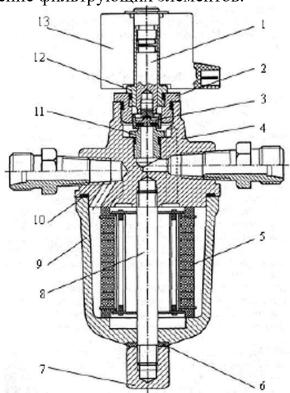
Электромагнитный клапан с фильтром газа: 1 - цилиндр: 2 - переходник: 3 - клапан дифференциальный: 4 - корпус; 5 - фильтрующий элемент; 6 - шайба; 7 - гайка колпака; 8 - шпилька; 9 - колпак фильтра: 10-кольцо уплотнительное: 11 - седло клапана; 12 - гильза; 13- катушка
